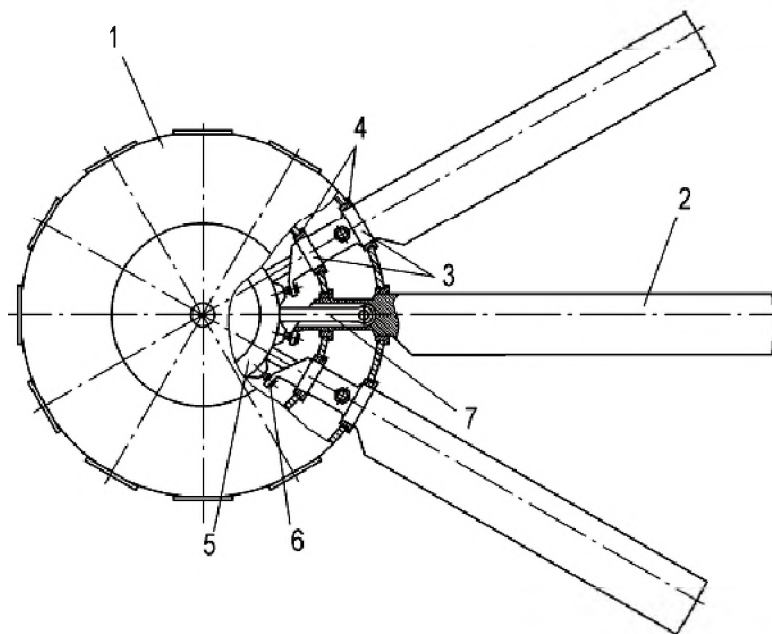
Компановка узлов РВ типа "винт в кольце":
